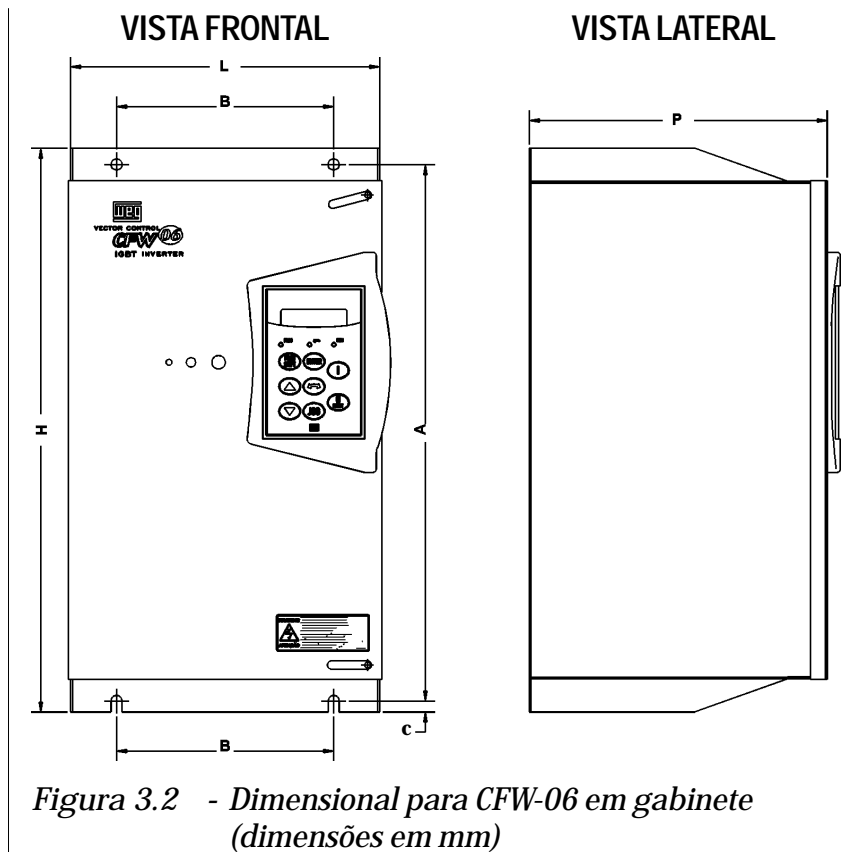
Dimensional para CFW-06 em gabinete (dimensões em mm)
